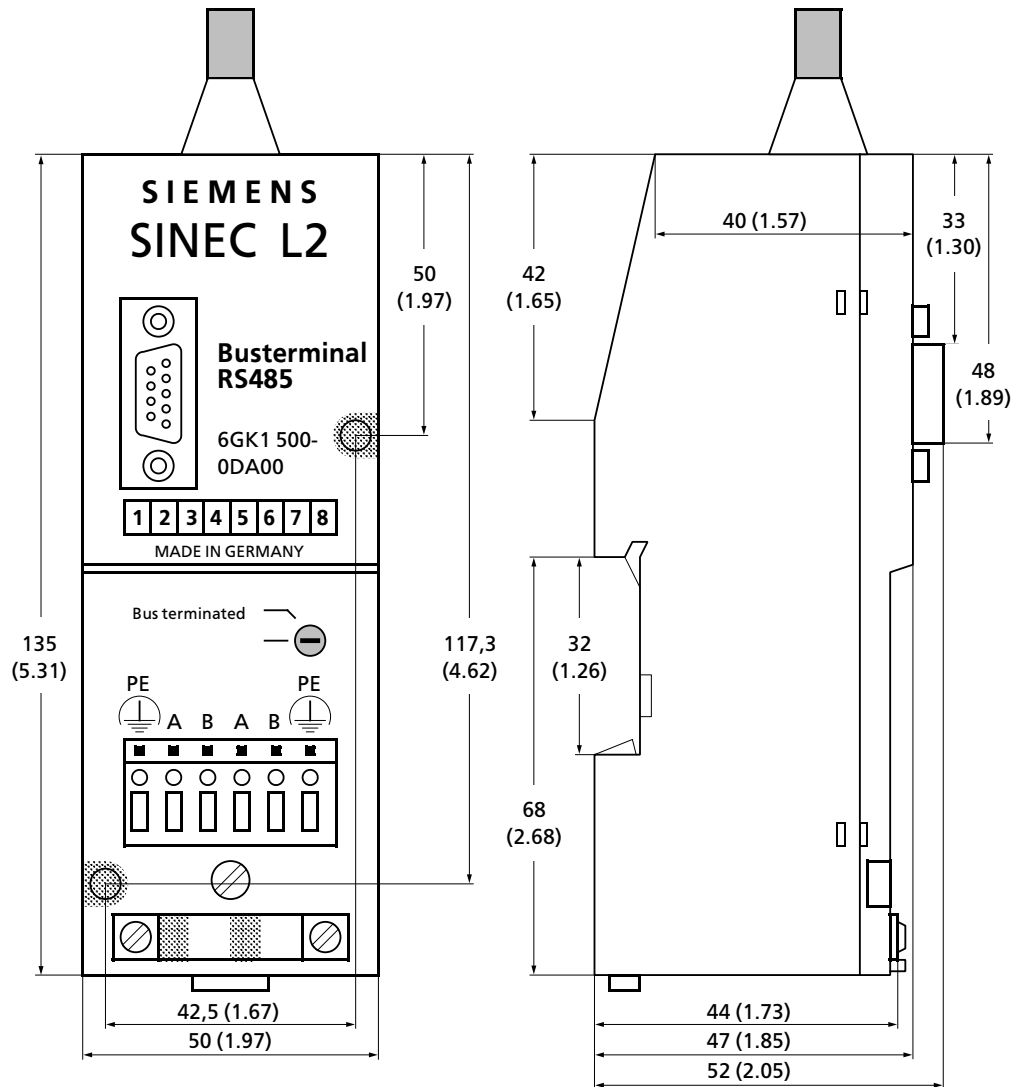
Abmessungen des SINEC L2- Buserminals (RS 485) mit aufgesetzter Bus-Schnittstelle
